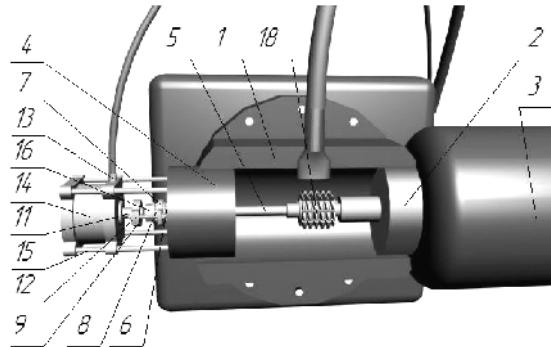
Супорт зубофрезерного верстата з пристроєм для підвищення жорсткості
